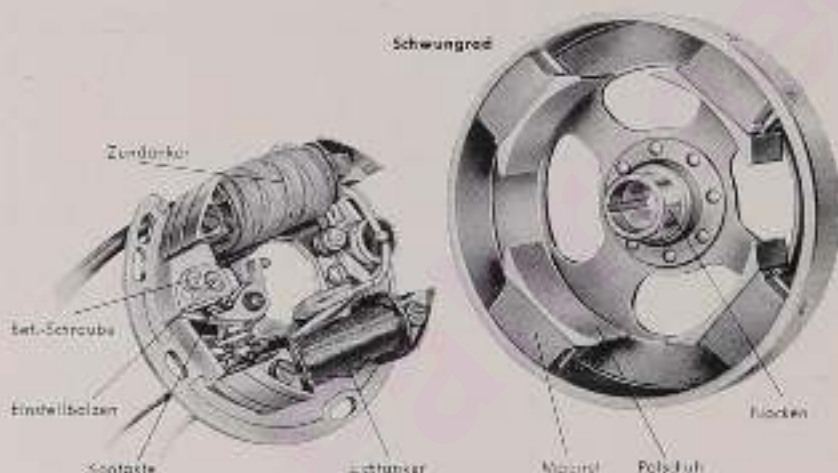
Bosch-Schwungradmagnetrüder (M/UTA 1/144/30) mit als Stahlblech gefertigtem Schwungrad
